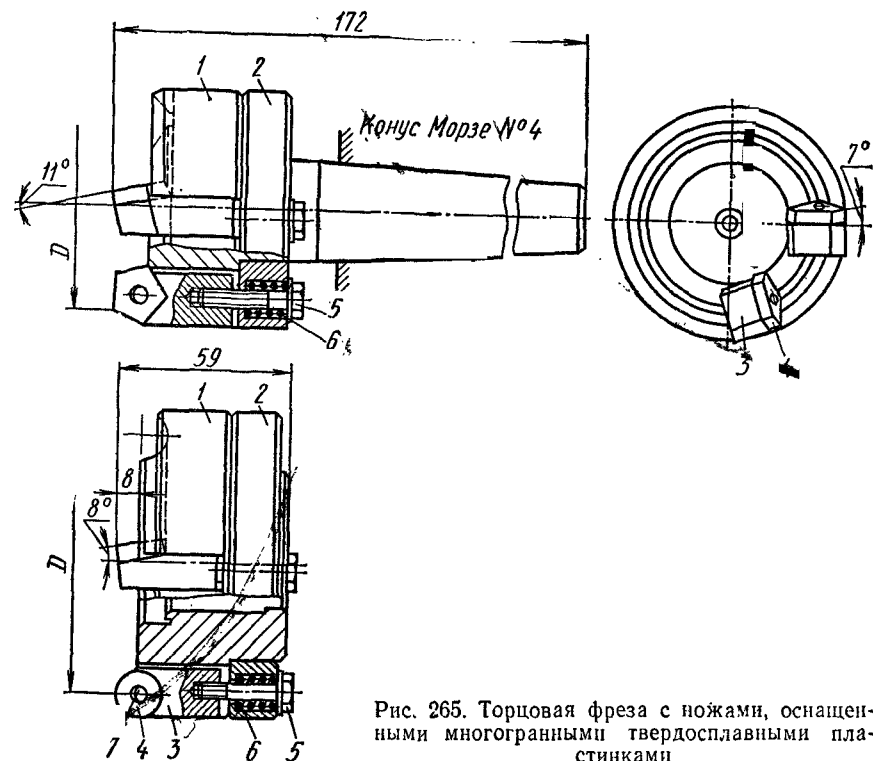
Торцовая фреза с ножами, оснащенными многогранными твердосплавными пластинками
